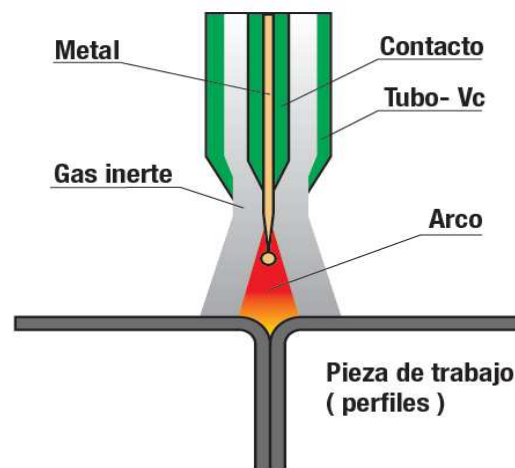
Esquema de aplicación de soldadura GMAW
